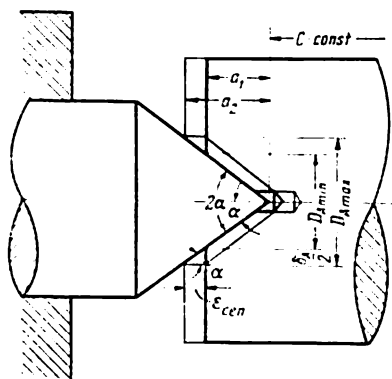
Enfoncement des pointes en fonction de la tolérance sur la cote du centre (la section au droit de la conjugaison de la pointe et du centre n'est pas hachurée par convention)
